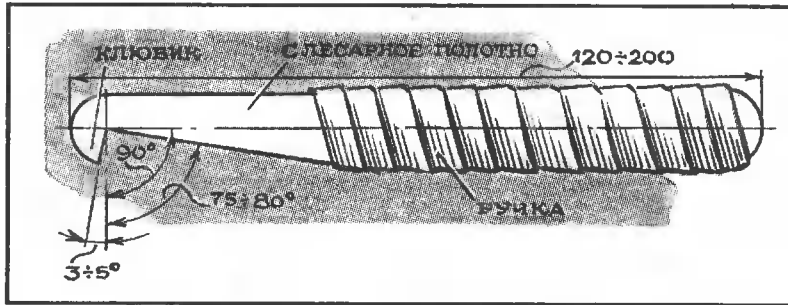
Резакон, сделанный из обломка полотна обычной слесарной ножовки.
